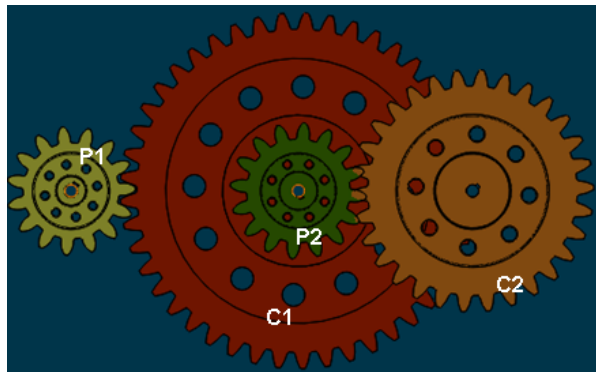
Ensamblaje Piñón – Corona, en base a diseño.
